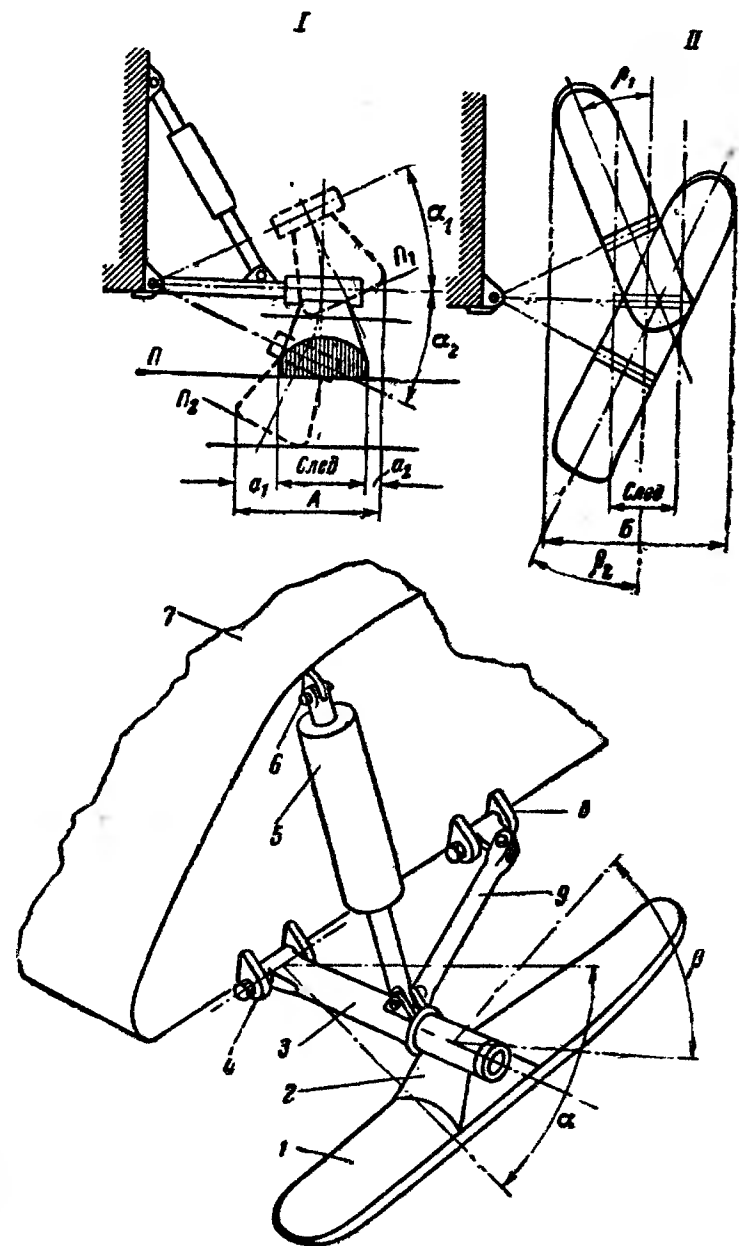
Кинематическая схема подвески лыж на полуосях: 1 — лыжа; 2 — кабанчик лыжи; 3 — полуось; 4 — осевой болт полуоси; 5 — амортизатор; 6 — узел крепления амортизатора к корпусу; 7 — корпус; 8 — узел разгрузочного подкоса; 9 — разгрузочный подкос; β — угол отклонения лыжи при вращении ее на полуоси; α — угол отклонения полуоси.
